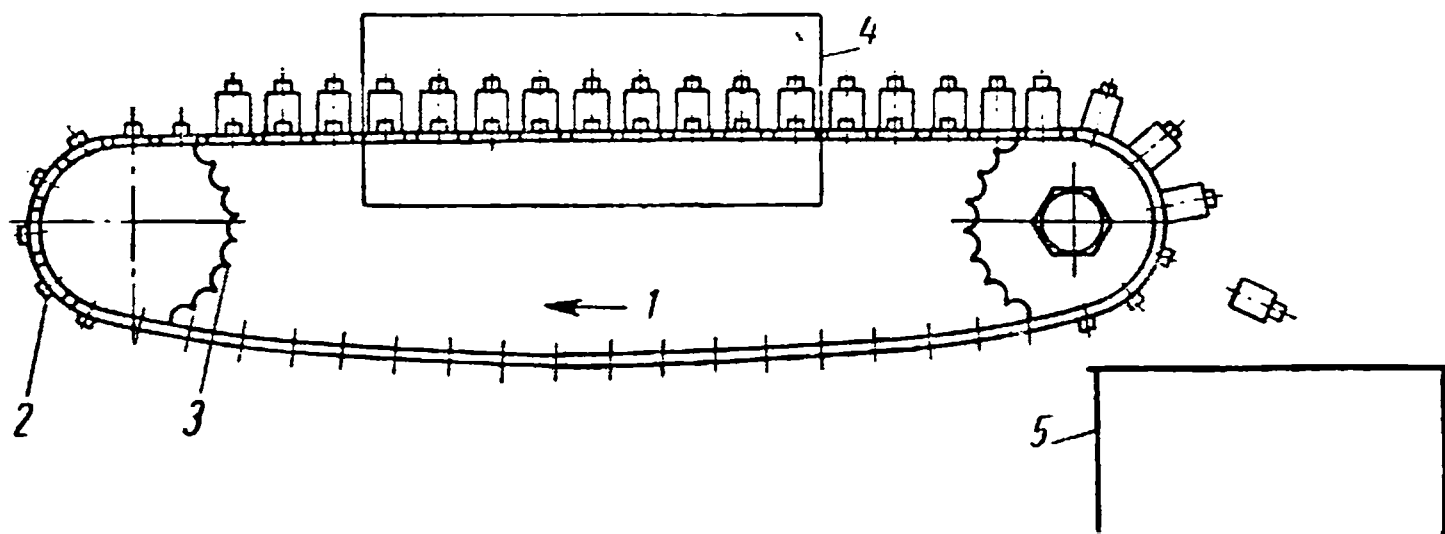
Схема установки конвейерного типа для газопламенной пайки
